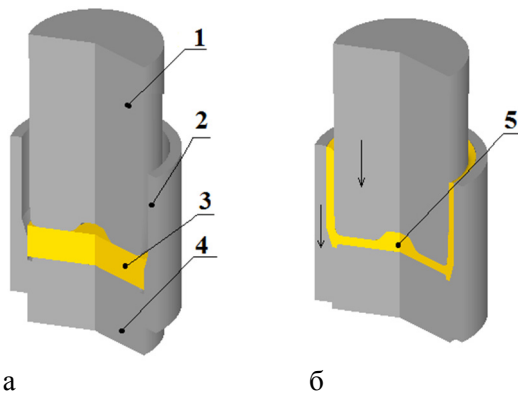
Розрахункові положення деформуючого інструмента та форма матриці: а – положення на початку штампування, б – положення в кінці штампування
